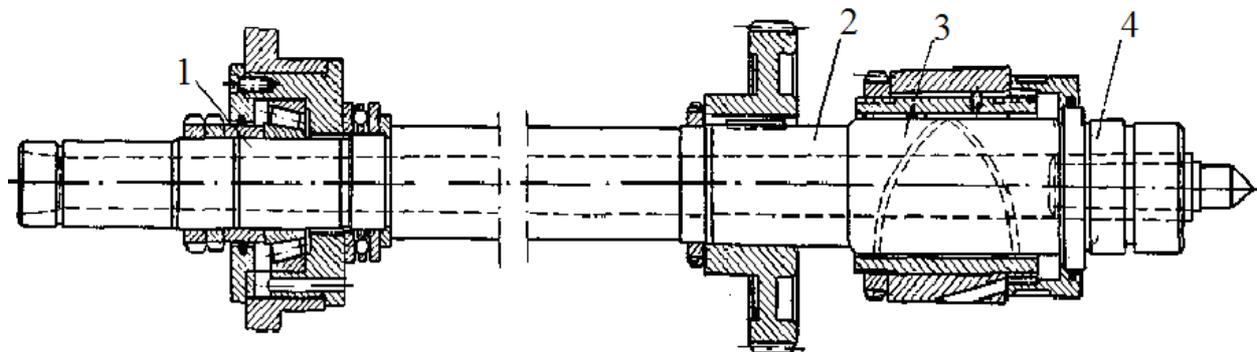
Типовая конструкция шпинделя токарного станка:
